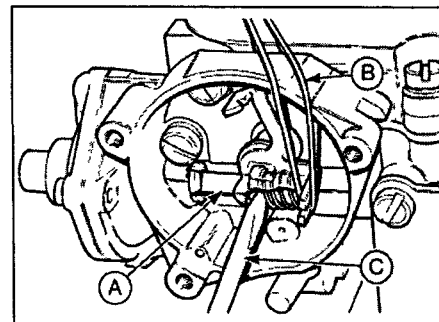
Установка рычага привода пускового устройства для проверки вакуумного привода
